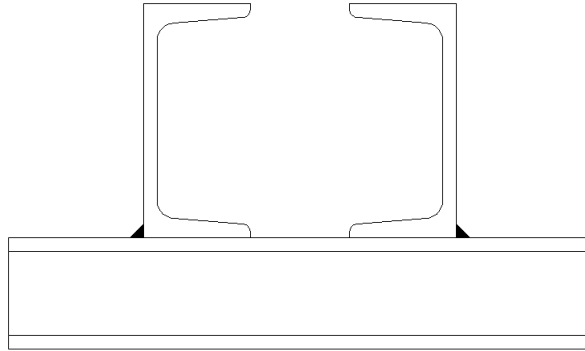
Esquema de la soldadura de la bancada del motor.
